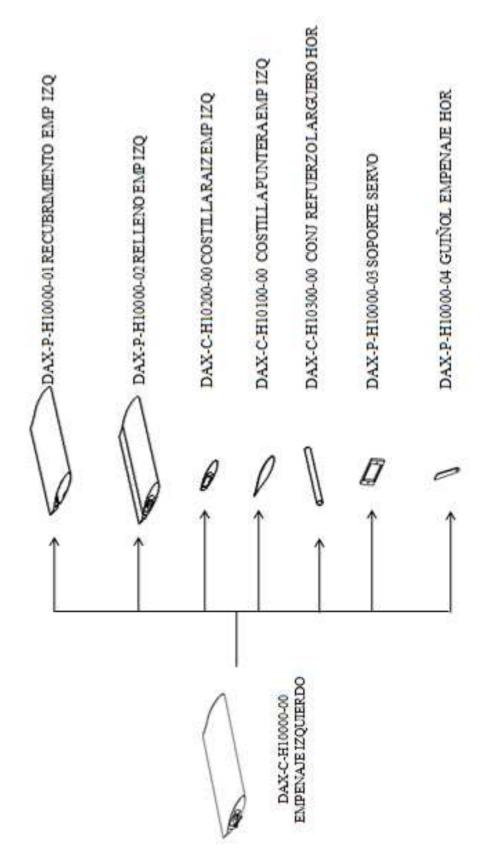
Subconjuntos del conjunto DAX-C-H10000-00 EMPENAJE IZQUIERDO.
